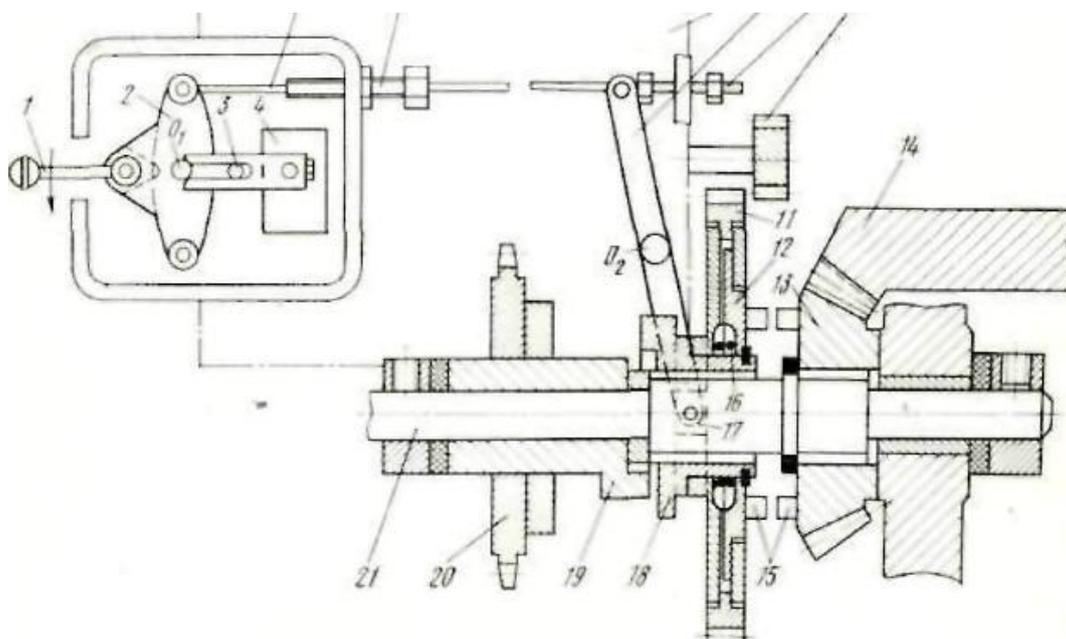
Устройство розыска раза на станке Г.ТР-8-250
